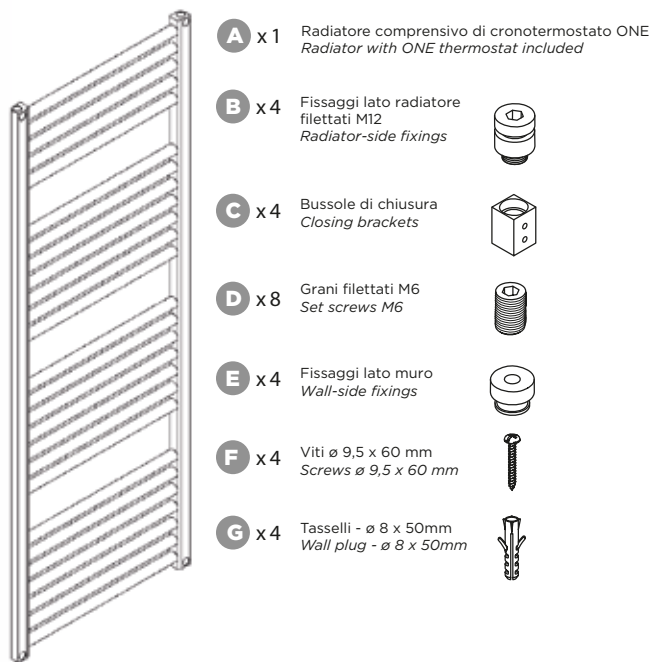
Necessario per l'assemblaggio/Necessary for assembly
